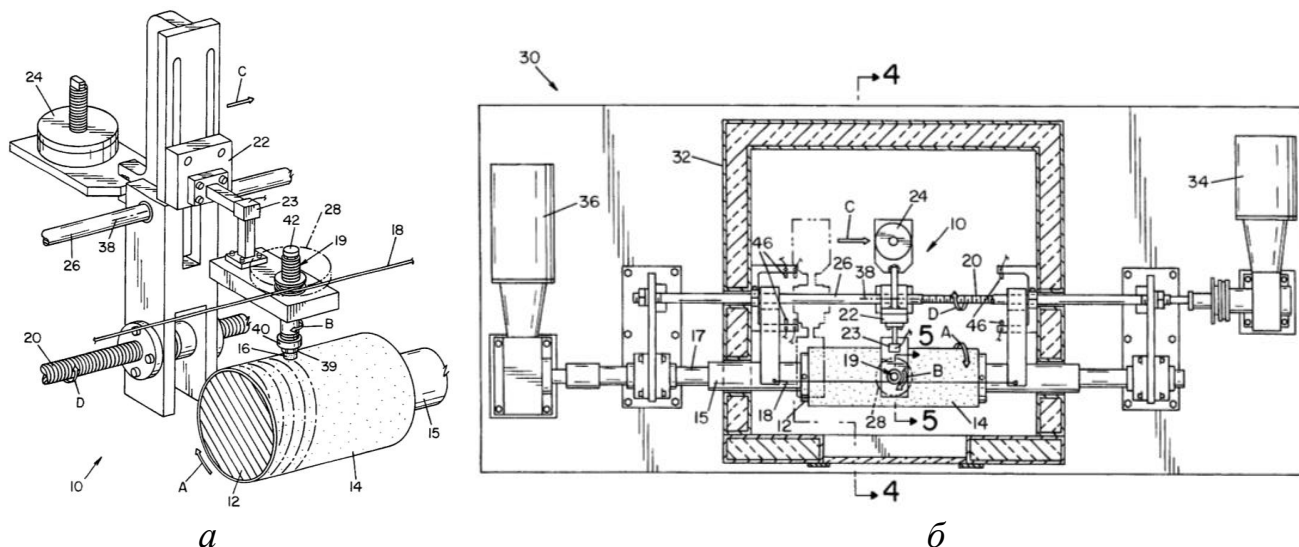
Общий вид устройства [154]: *а* – часть устройства для переноса образца; *б* – вид устройства сверху в разрезе; 12 – барабан; 14 – абразивная поверхность; 15 – рукав; 16 – испытуемые образцы; 17 – ось; 18 – кабель; 19 – шпиндель; 20 – резьбовой винт; 22 – держатель образцов; 23 – датчик веса; 24, 28 – вес; 26 – вал; 34, 36 – двигатели; 32 – экологическая камера; 38 – точка вращения; 39 – цанга; 40 – цанговая гайка; 42 – регулируемый винт; 46 – датчик освещенности
